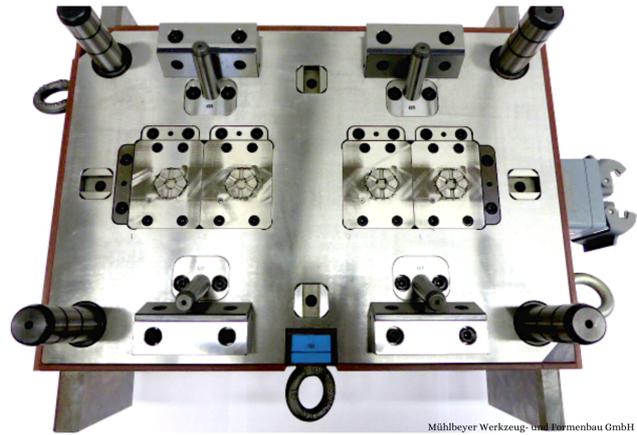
Spritzgießwerkzeug 4-fach Düsenseite für kunststoffummantelter Stator
